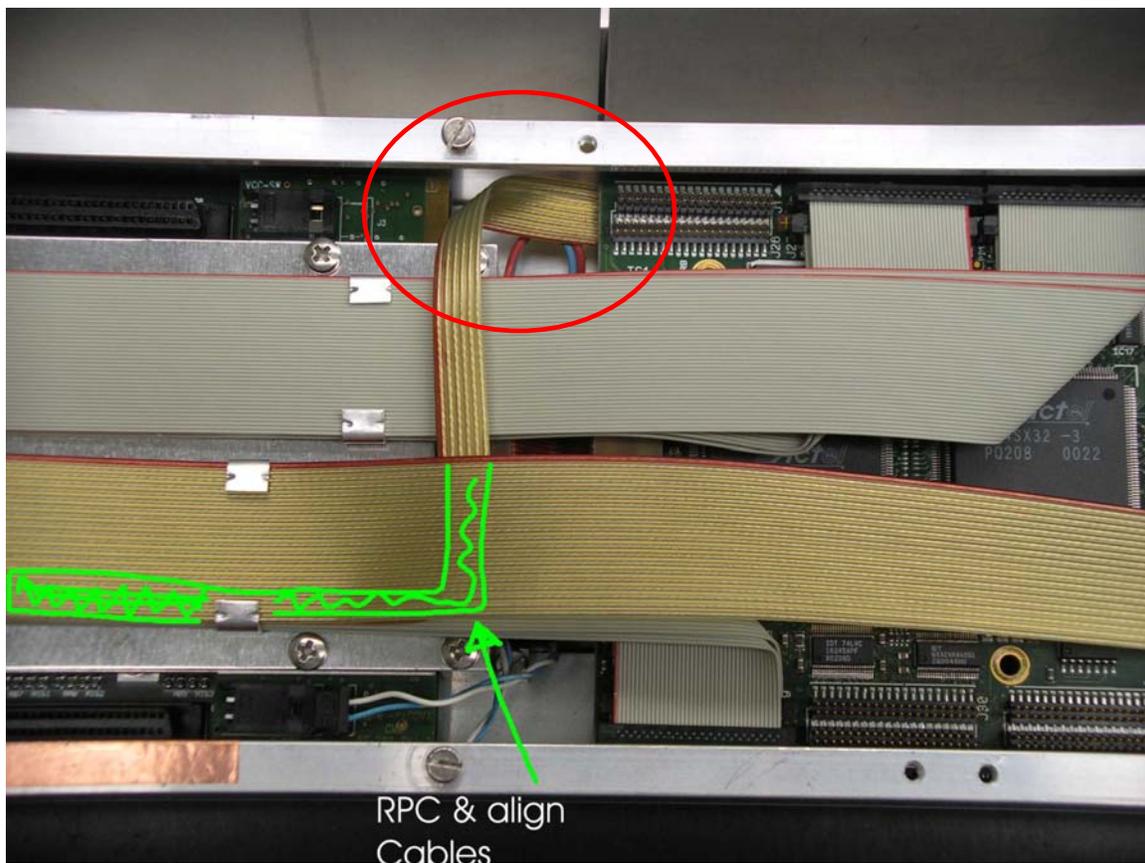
Cables routing in uscita dalla SB. Dettaglio su cavi RPC e Allineamento.
